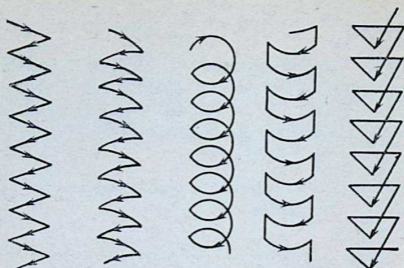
Движения электрода при ручной электродуговой сварке.
